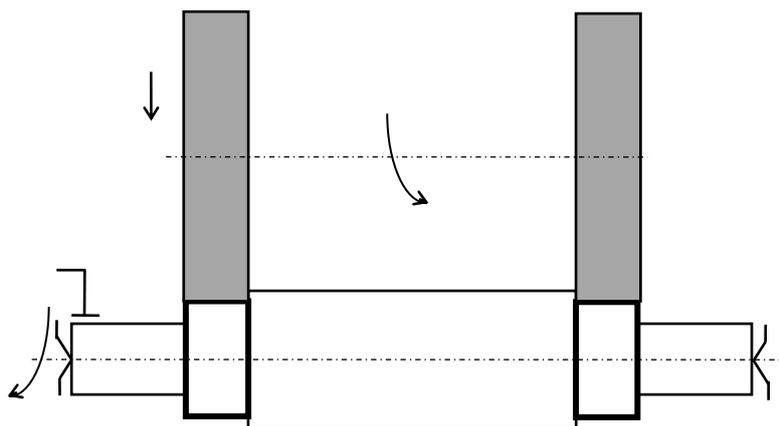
Эскиз финишной операции по обработке вала - шлифование шеек
